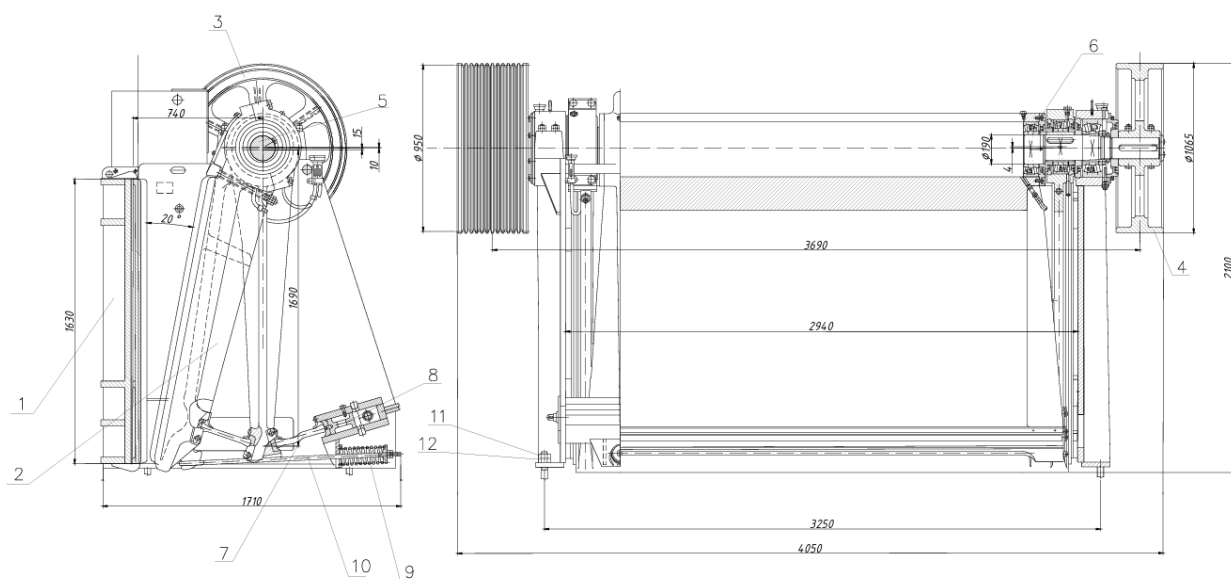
Щокова дробарка зі складним рухом щоки типу ЩДС :
